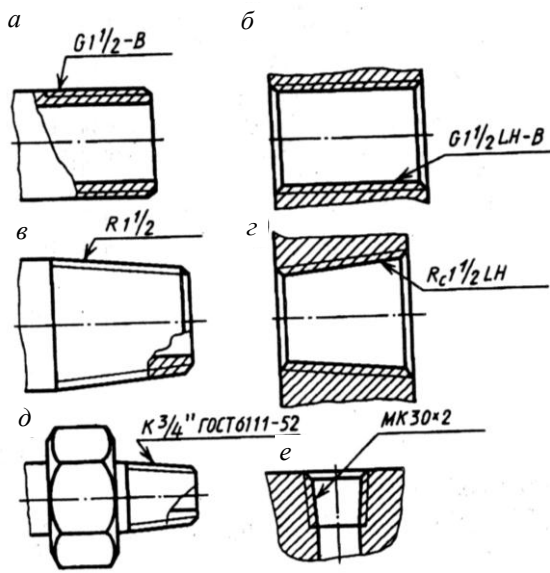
78. Условные обозначения трубной и конической резьб:
